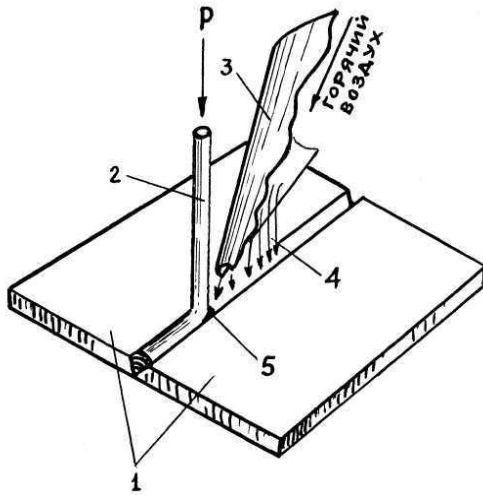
Схема сварки нагретым газом с использованием сопла для ускоренной сварки: 1 – свариваемые заготовки; 2 – присадочный пруток; 3 – сопло для подачи горячего газа; 4 – распределение горячего газа в зоне подогрева и сварки; 5 – валик тестообразного материала
